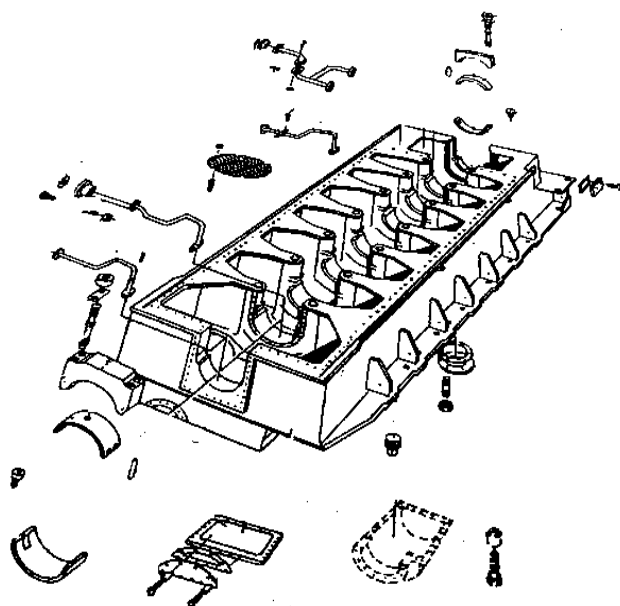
Фундаментна рама двигуна 6ДКРН 80/230
